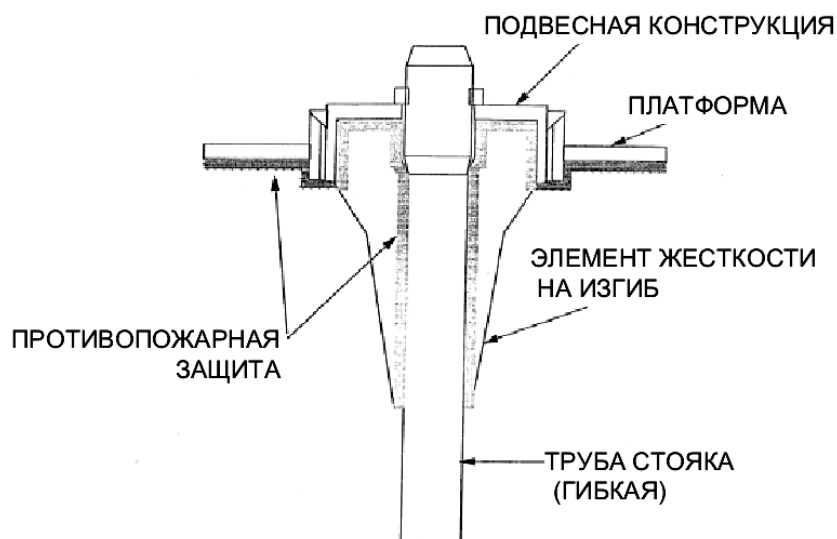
Устройство защиты противопожарной для гибкого трубопровода и конструкций подвесных
